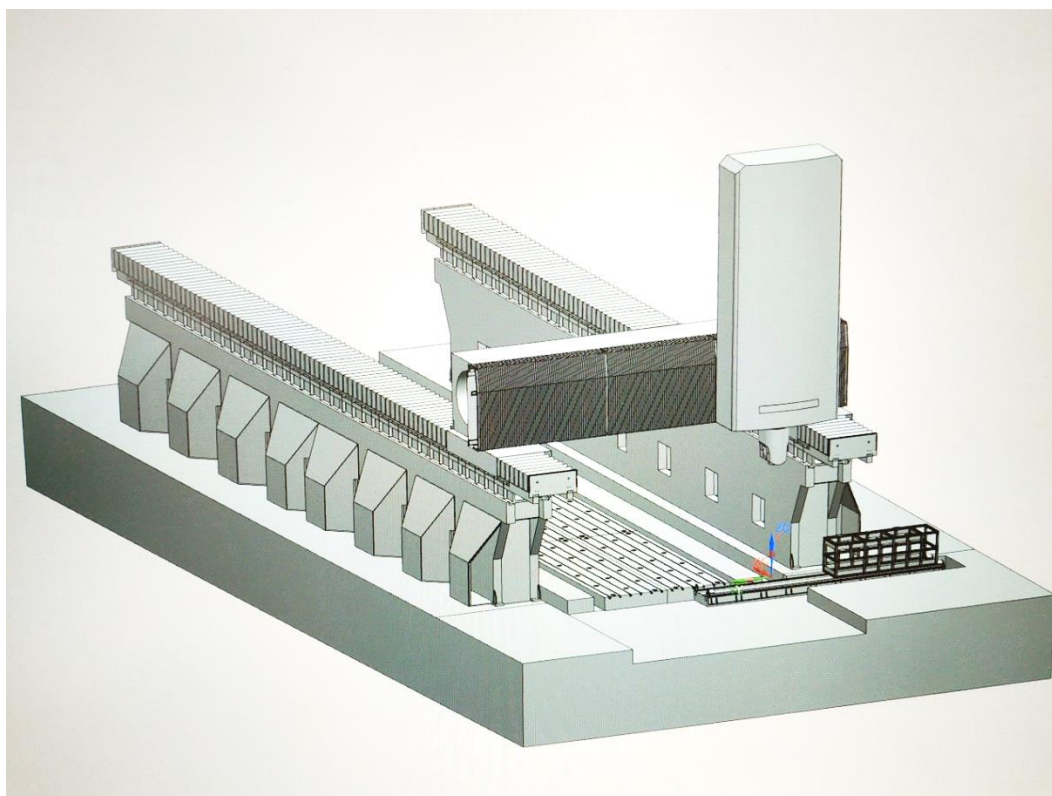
5-ти координатный станок с ЧПУ и подвижной головкой.
